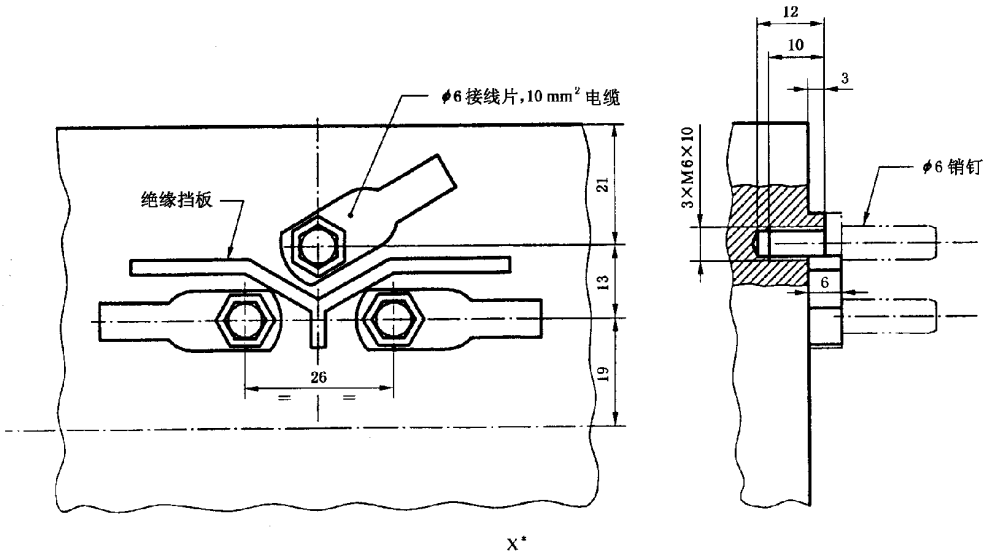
用于 H 型变压器连接的 3 个 M6 孔的尺寸和位置
